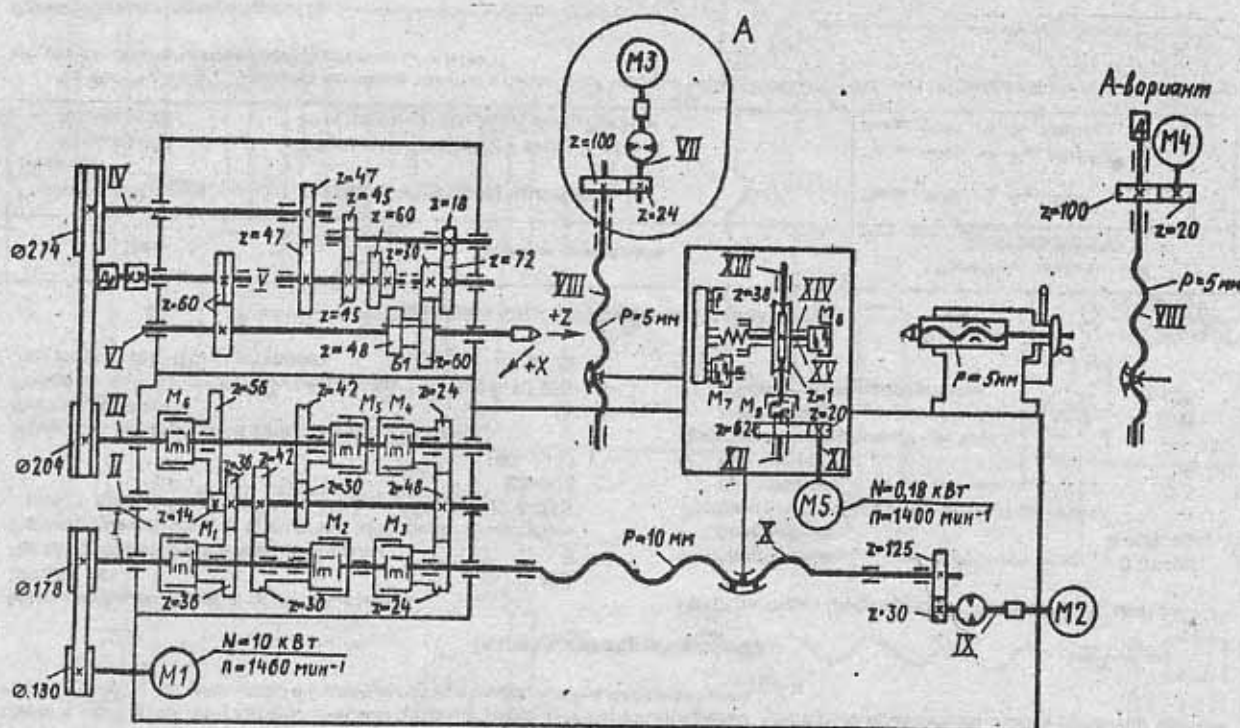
Кинематическая схема токарного патронно-центрального станка мод. 16K20Ф3С5 с ЧПУ
